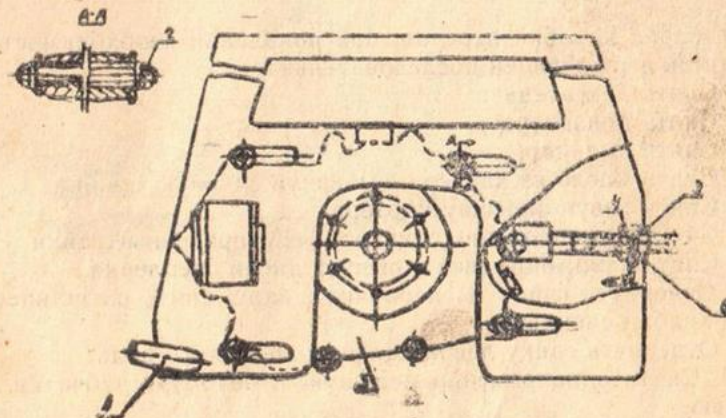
Схема натяжения цепной передачи с двигателя на редуктор:
